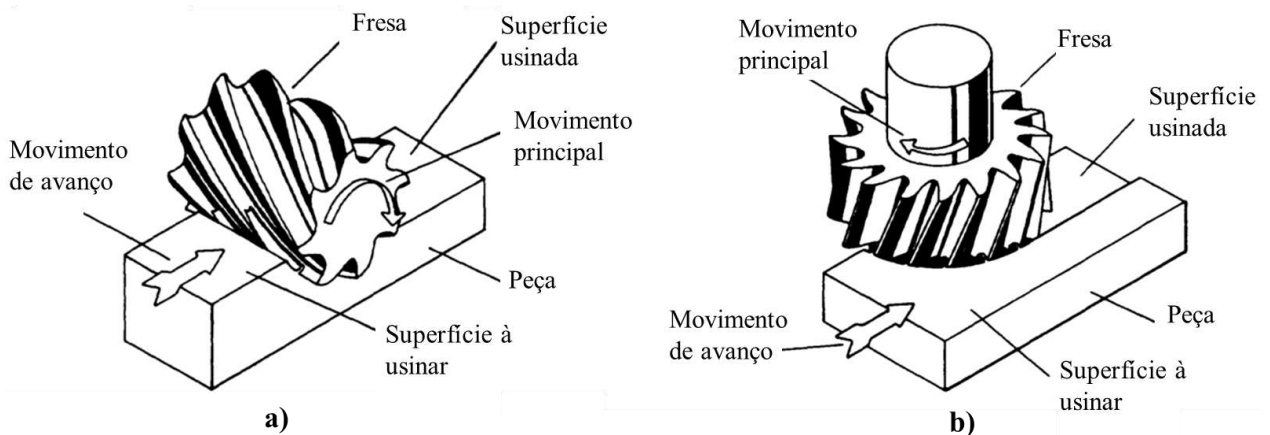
a) Fresagem tangencial e b) Fresagem frontal
